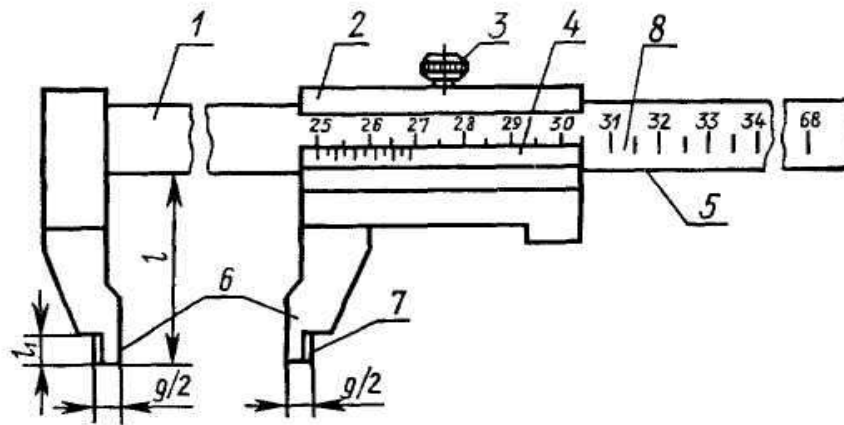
1 – штанга; 2 – рамка; 3 – затискувач; 4 – ноніус; 5 – робоча поверхня штанги; 6 – губки з плоскими вимірювальними поверхнями для вимірювання зовнішніх розмірів; 7 – губки з циліндричними вимірювальними поверхнями для вимірювання внутрішніх розмірів; 8 – шкала штанги
